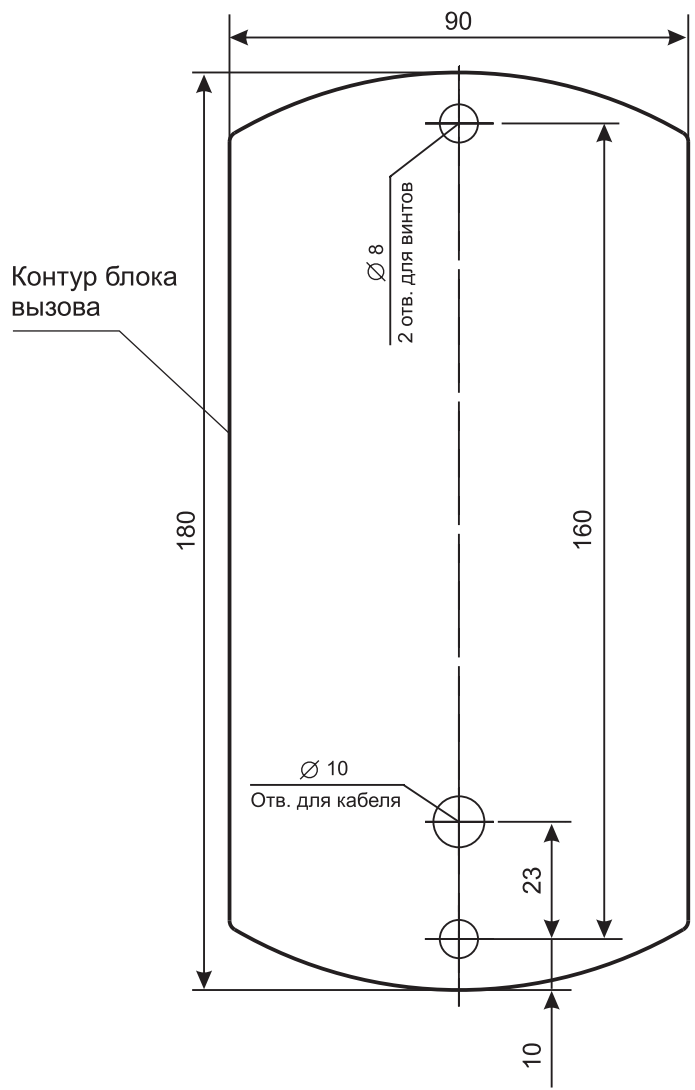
Расположение и размеры отверстий для установки блока вызова
